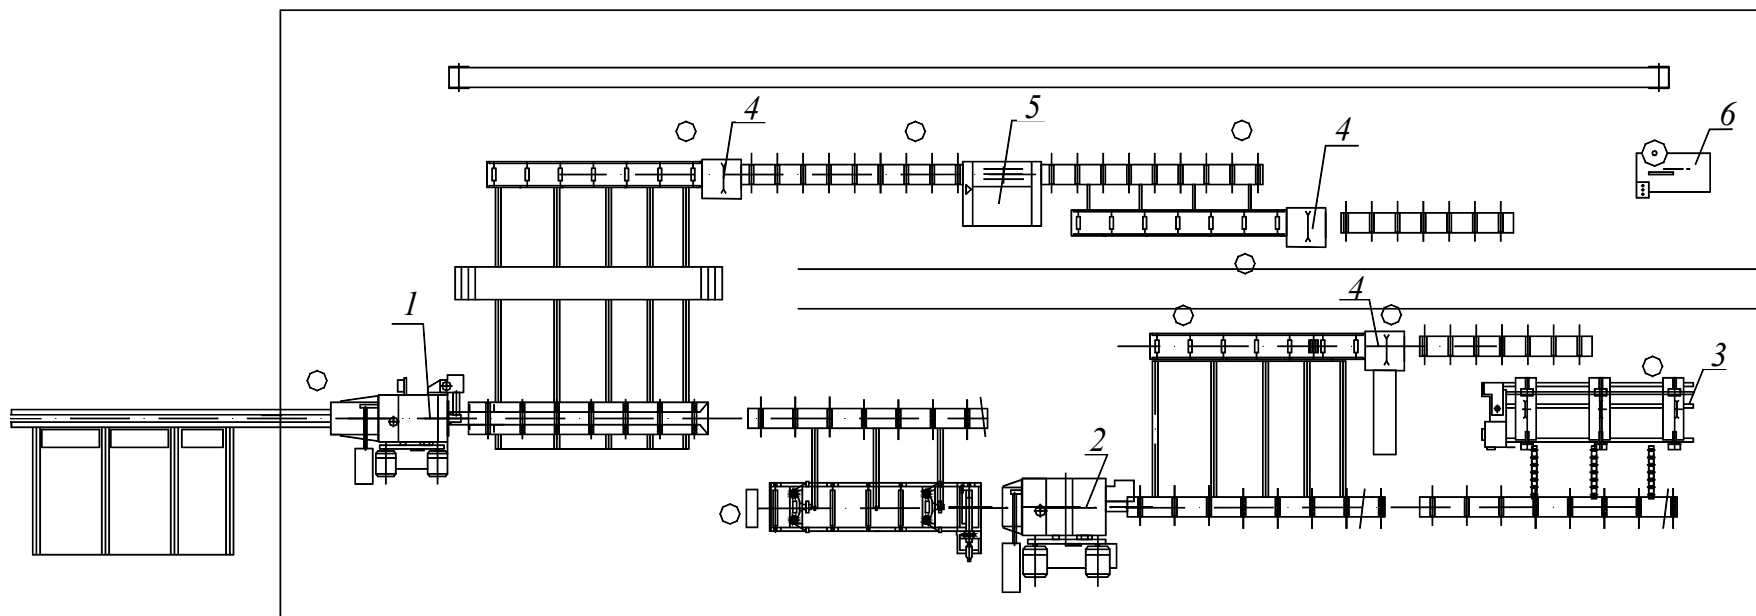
Схема расположения оборудования в цехе на базе многопильных круглопильных станков:
